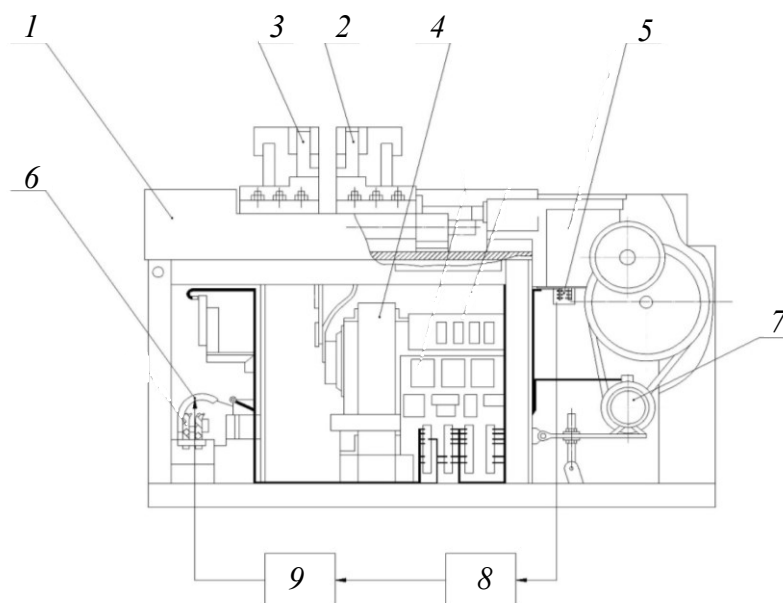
Общий вид машины для контактной стыковой сварки МС-2008М:
